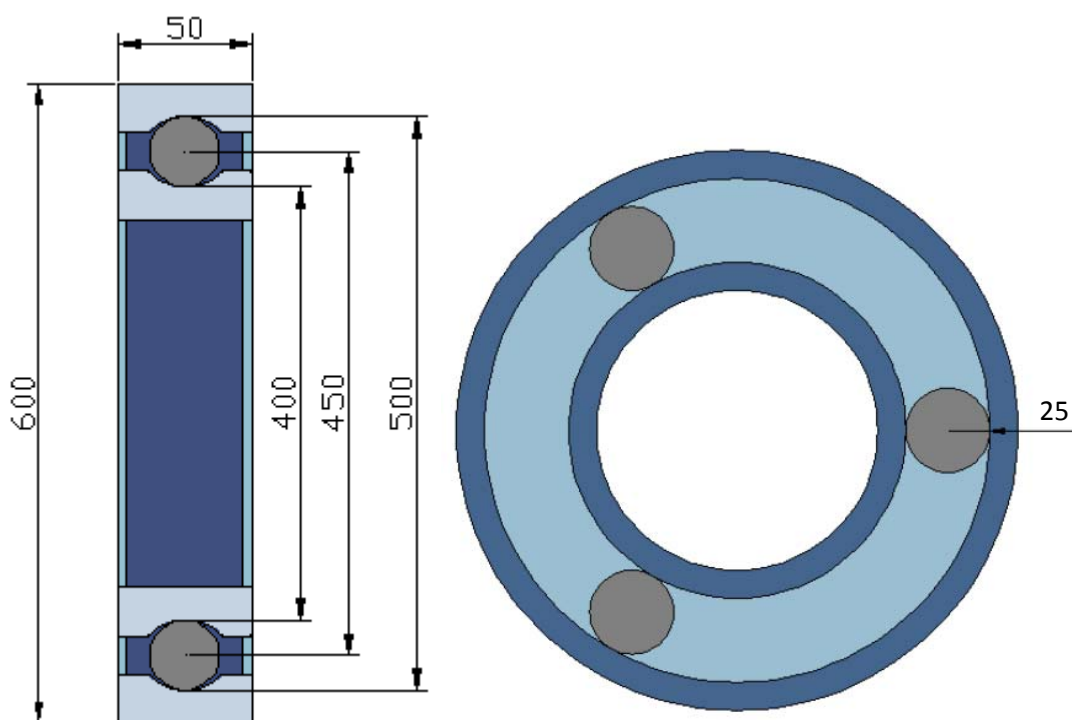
Esquema y dimensiones del rodamiento de 3 bolas
